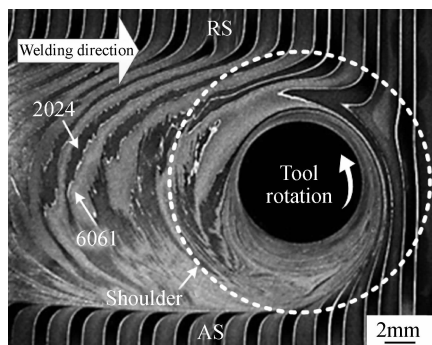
垂直焊缝排列匙孔附近材料流动宏观形貌
